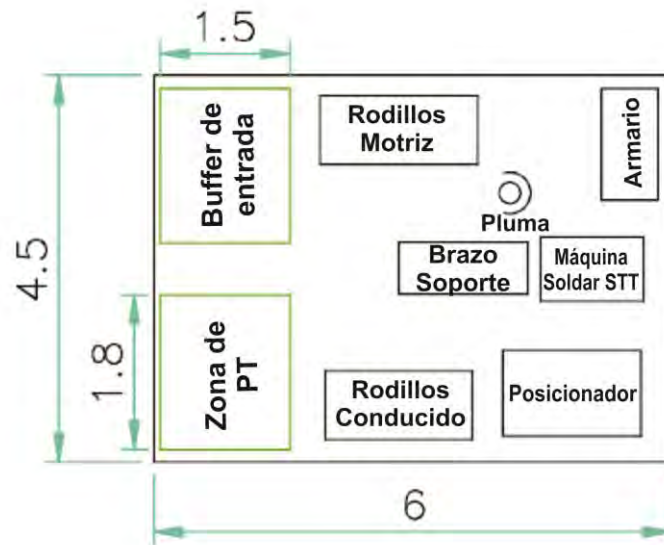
Diseño de estación de trabajo Soldadura Pase Raíz
